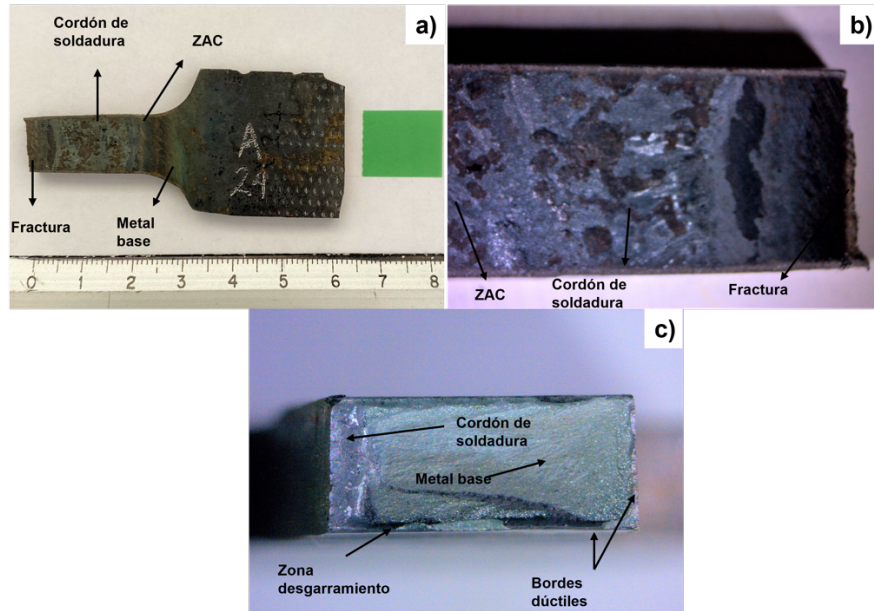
Fractografía estereoscópica para unión GTAW24 donde a) en vista macroscópica se observa la unión soldada de la sección de agarre a la fractura, b) vista longitudinal de la zona fracturada, c) vista transversal a 6.5x con fractura en el metal base
